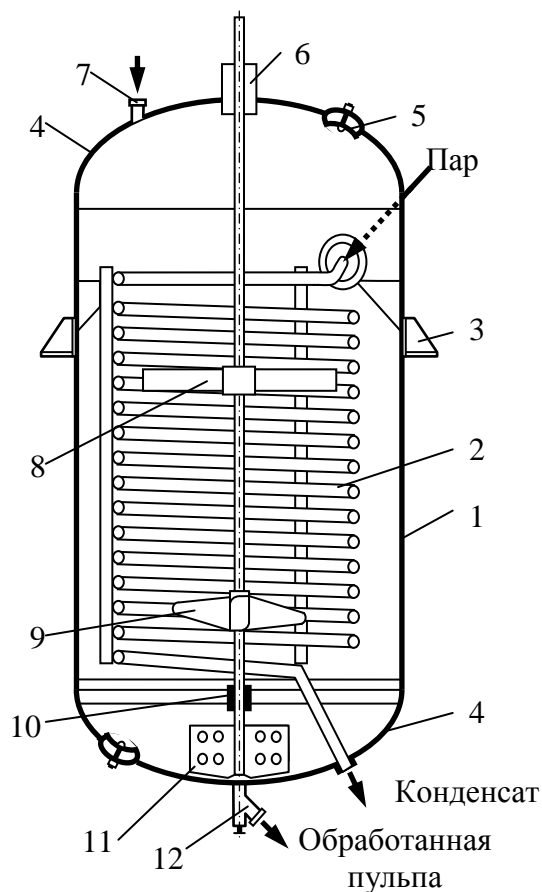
Автоклав: 1 – корпус; 2 – теплообменник змеевикового типа; 3 – опора; 4 – сферическая крышка и днище; 5 – ремонтный люк; 6 – корпус сальника; 7 – горловина; 8 – перемешивающее устройство лопастного типа; 9 – перемешивающее устройство пропеллерного типа; 10 – нижний подшипник; 11 – перемешивающее устройство листового типа; 12 – разгрузочный вентиль
